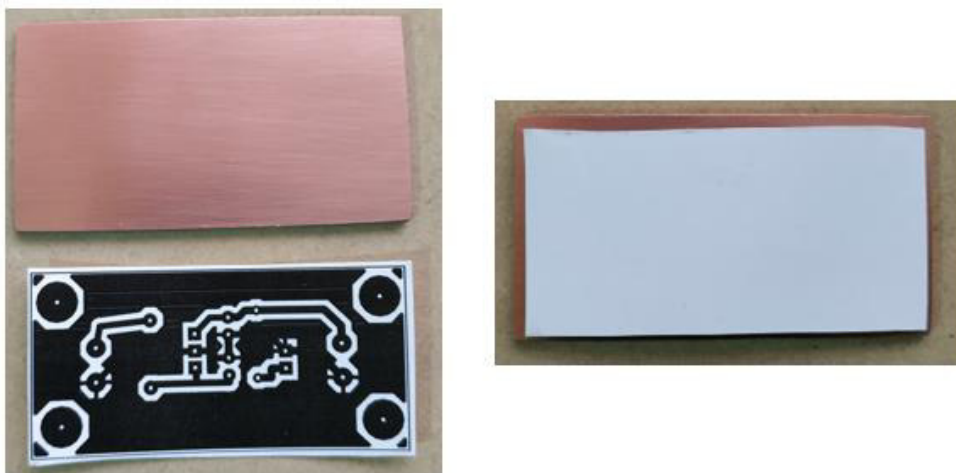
Implementación de la impresión PCB sobre baquelita
